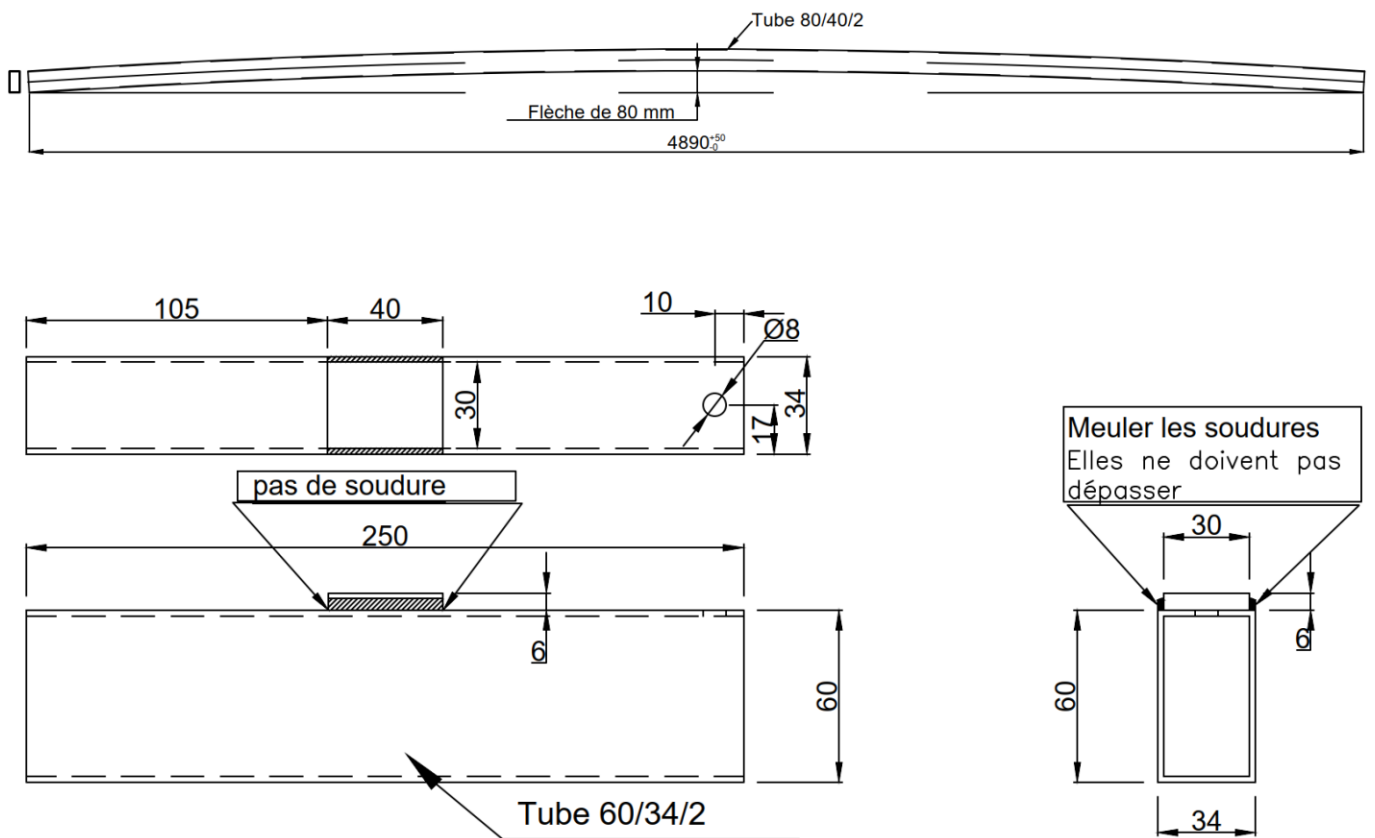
Schéma des barres de tension de toiture et manchons intermédiaires
